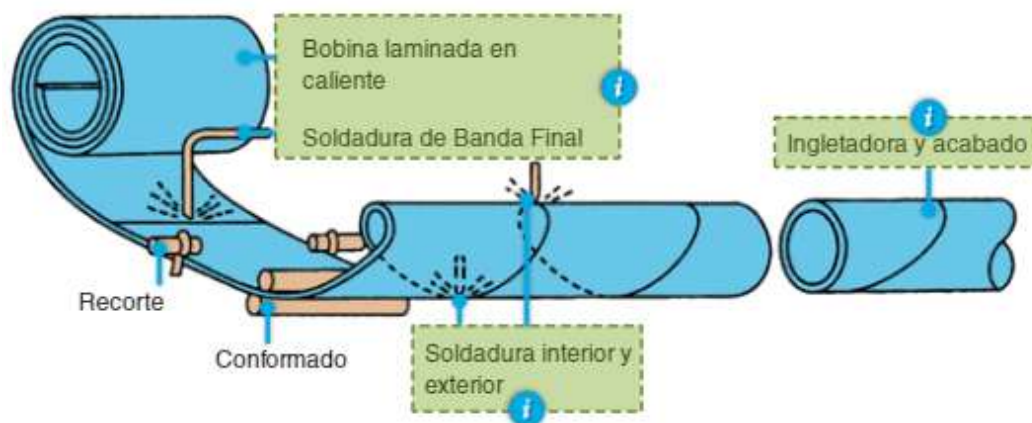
Soldadura de tubos en espiral [27].
